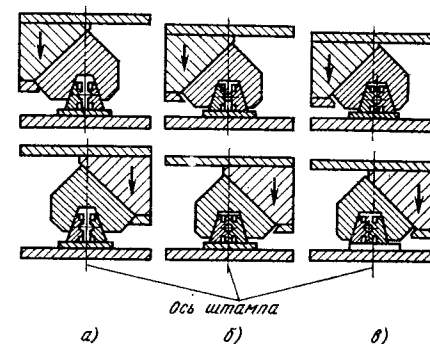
Схема работы штампа для не полностью закрытой отрезки с дифференцированным зажимом: а — исходное положение; б — пруток зажат; в — отрезка заготовки
